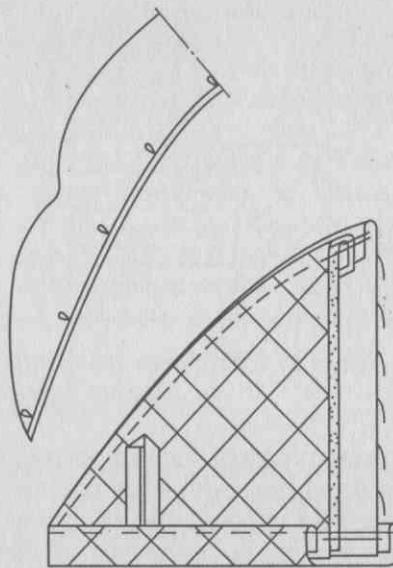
Схема сборки съемного шалевого воротника, пристегивающегося к воротнику изделия на навесные петли и пуговицы
